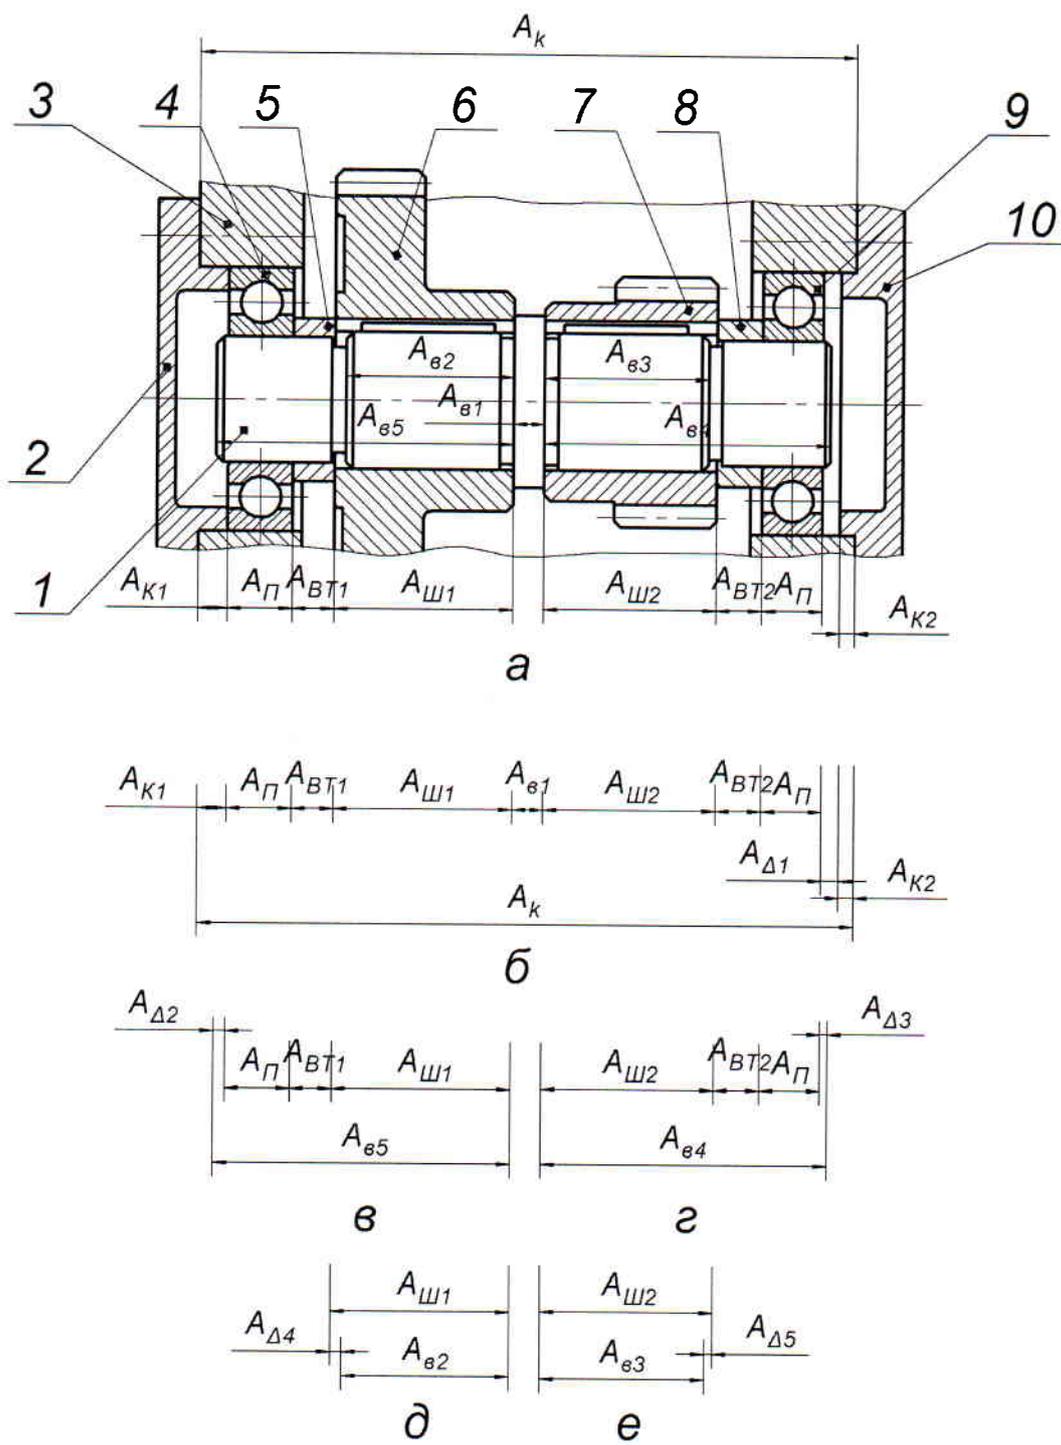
Узел механизма (а) и сборочные размерные цепи (б–е)
